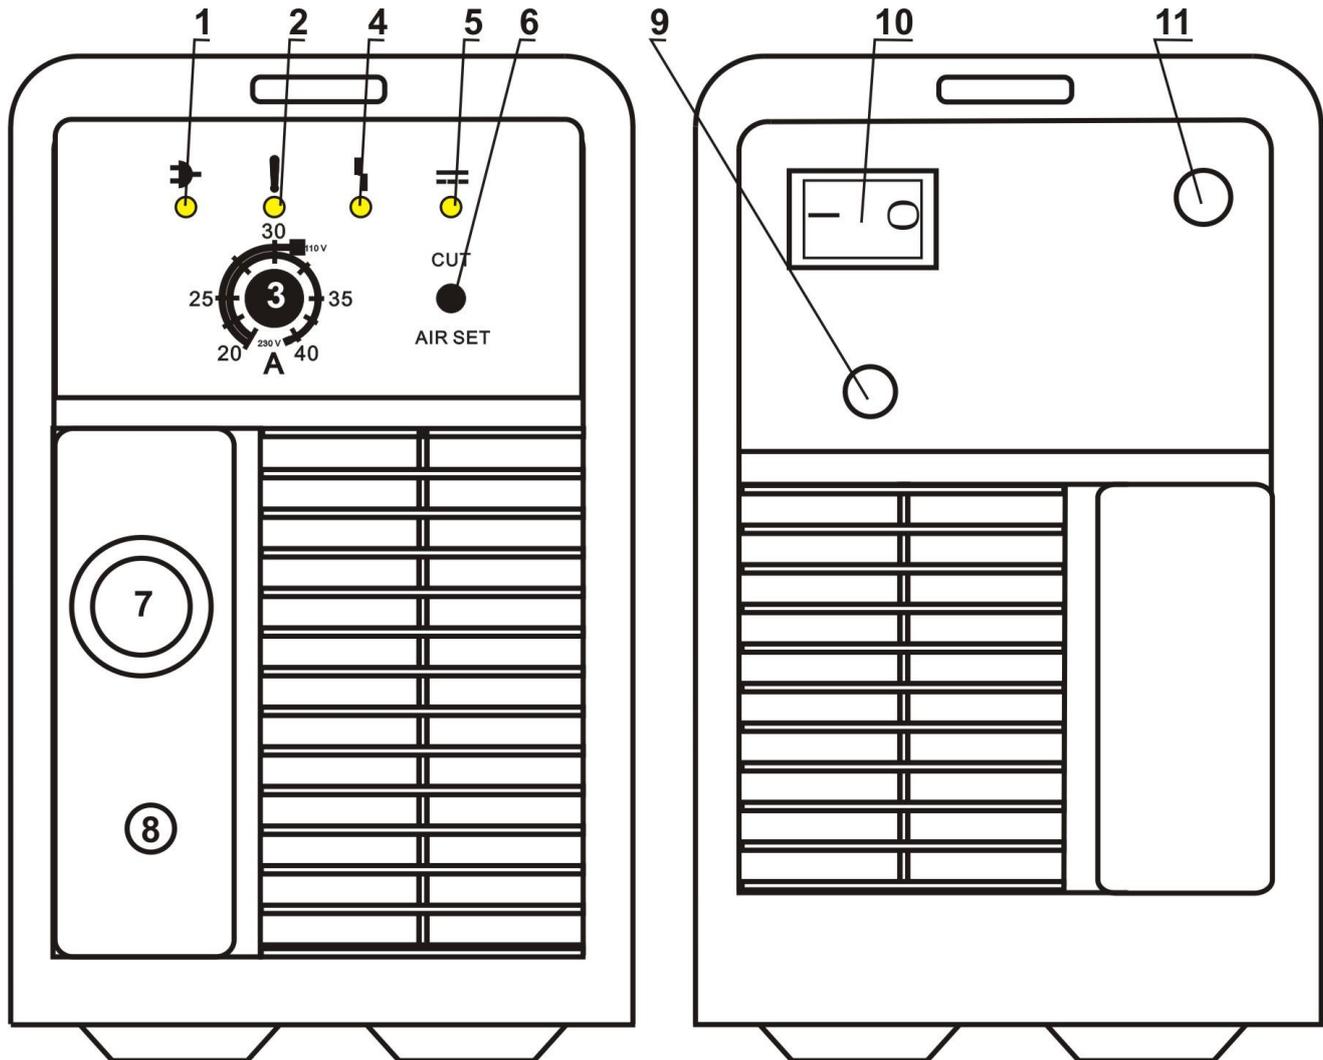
Hauptteile der Maschine, Front- und Rückansicht.
